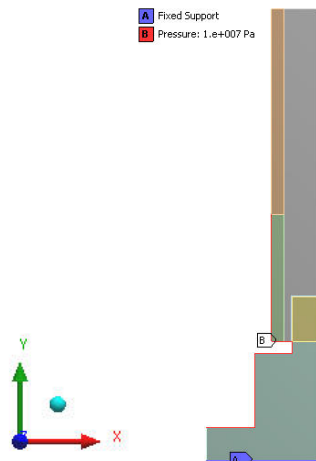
Сечение корпуса гидроцилиндра с внешними нагрузками
